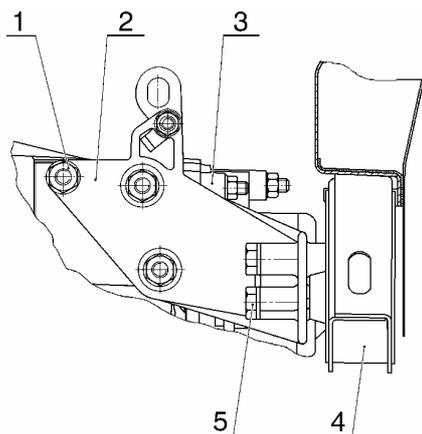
Левая опора подвески двигателя автомобиля ВАЗ-11183:
